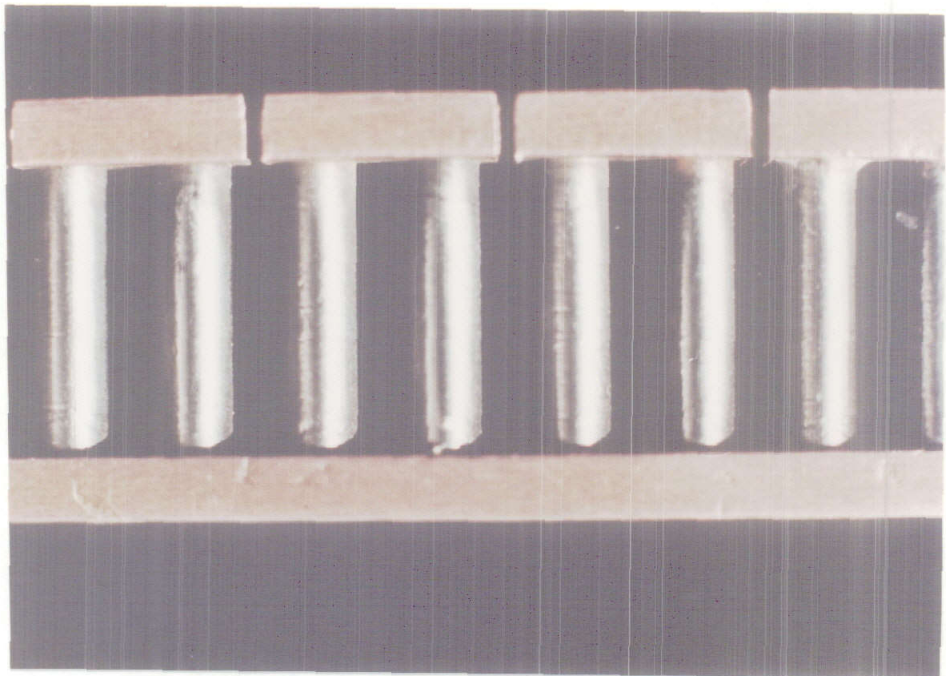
Detalle de las soldaduras del fluxímetro de calor
